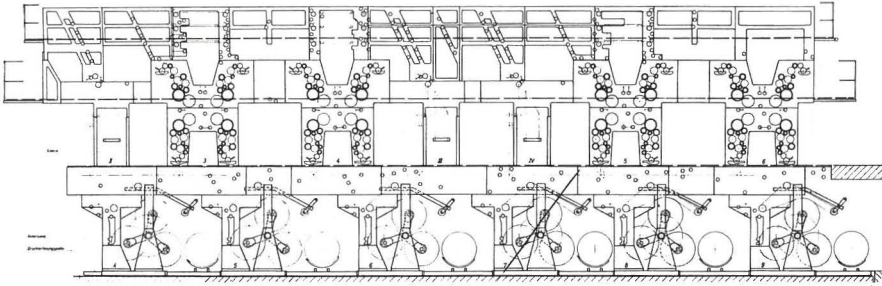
Rollen-Hochdruckmaschine in Unterbauausführung
